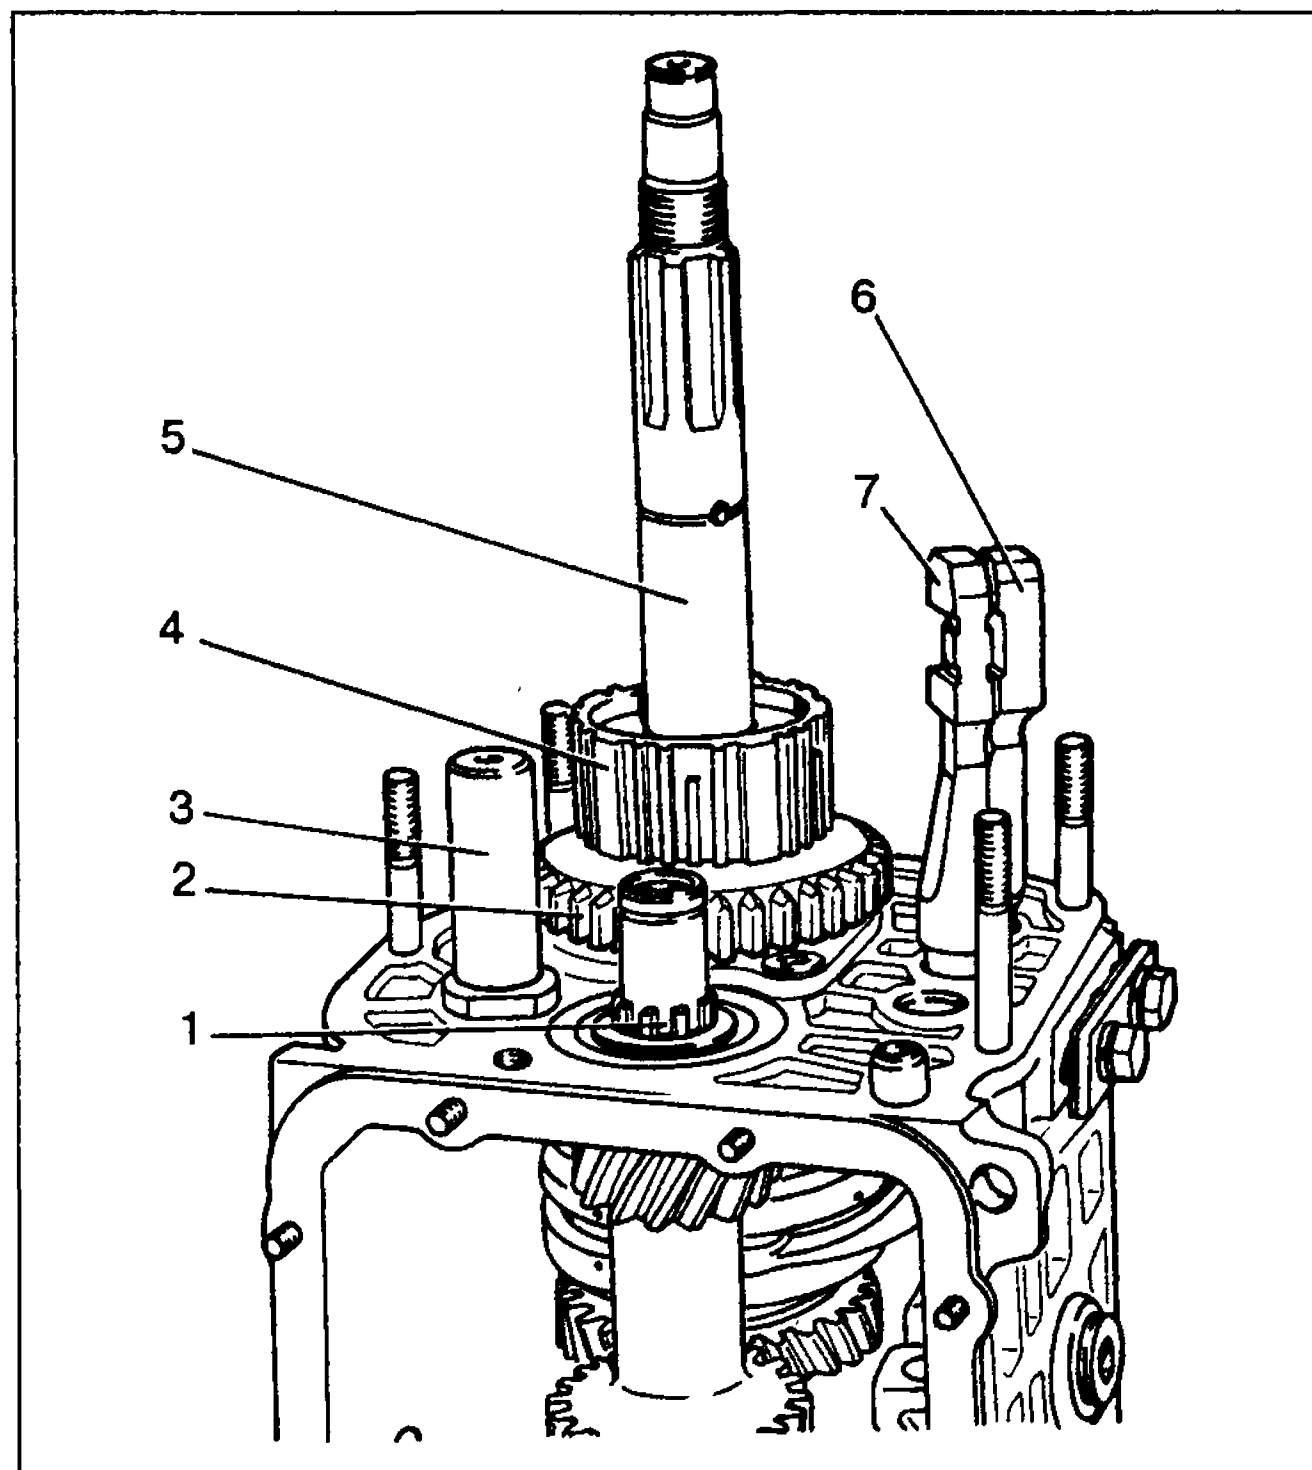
Снятие штока вилки включения V передачи и заднего хода и блока шестерен:
